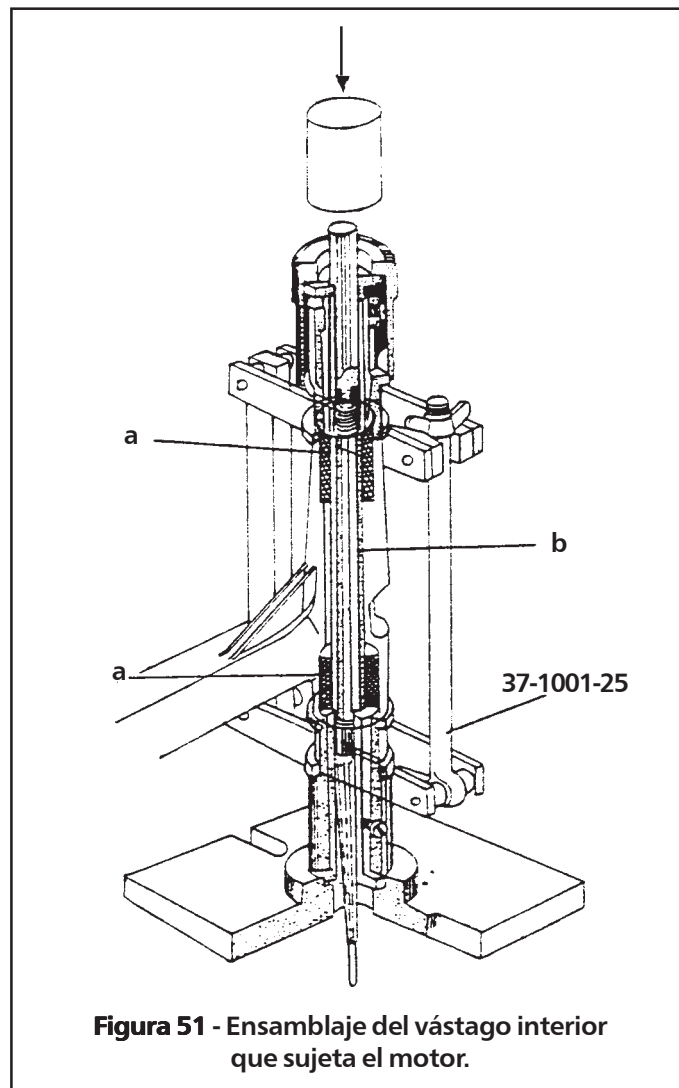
Ensamblaje del vástago interior que sujeta el motor.
